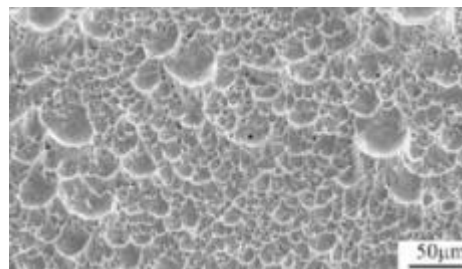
Rotura dúctil de la unión soldada de un tanque (NASA)
